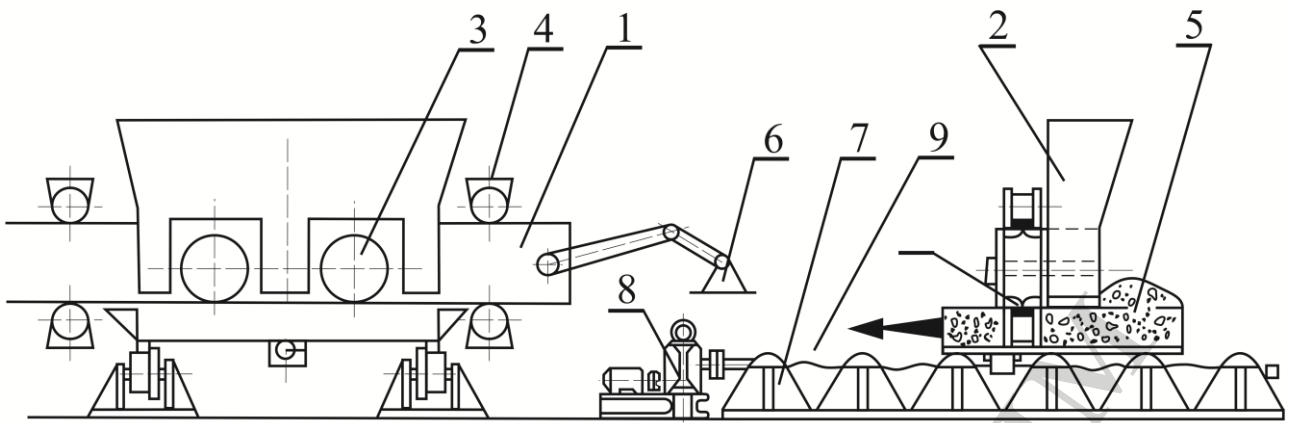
Конструктивна схема пристроїв роликового формування: 1 – балка; 2 – витратний бункер; 3 – формувальні ролики; 4 – направляючі; 5 – форма; 6 – кривошипно–шатунний механізм; 7 – рольганг; 8 – привід переміщення форми; 9 – ходовий гвинт
